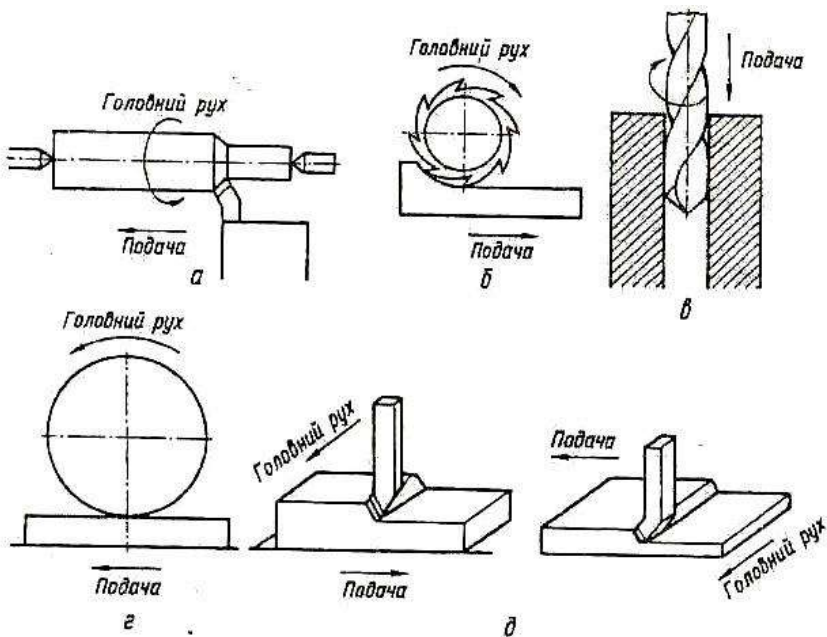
Основні види обробки металів різанням: а – точння; б – фрезерування; в – свердління; г – шліфування; д – стругання
